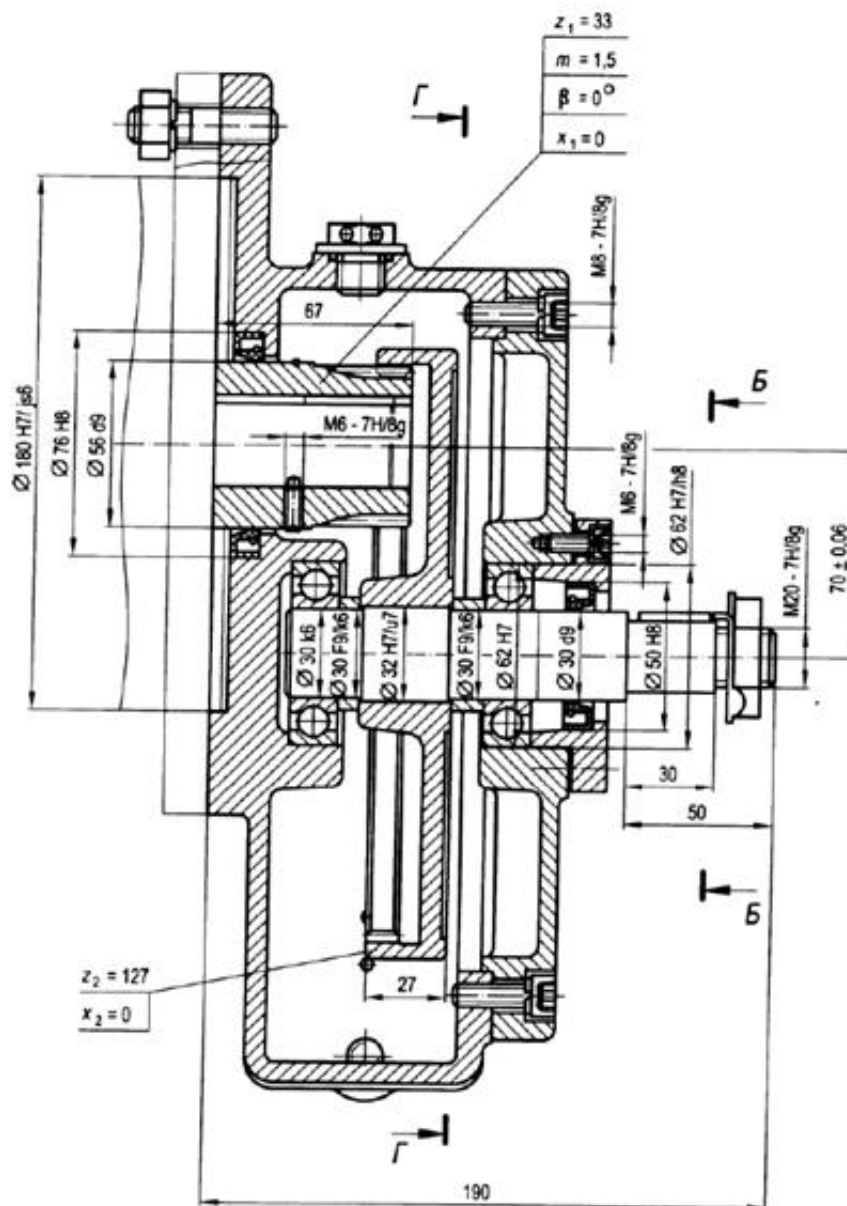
Мотор-редуктор цилиндрический одноступенчатый [4]
